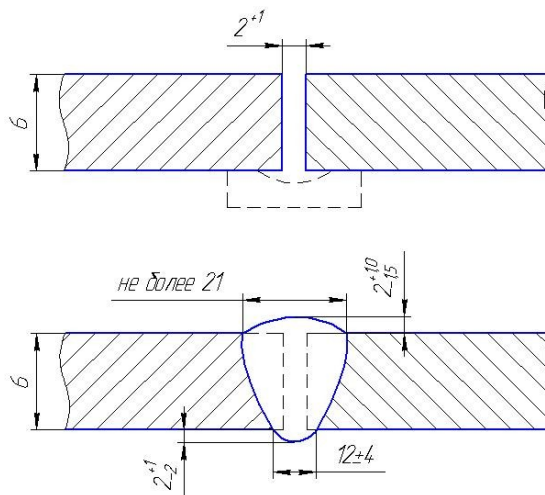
Сварное соединение для элементов бака ВБР-25
